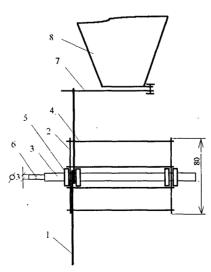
Барабан прикормки: 1 — спица; 2 — щечки; 3 — вал; 4 — распорки; 5 — гайки; 6 — отверстие под шплинт; 7 — задвижка; 8 — бункер
